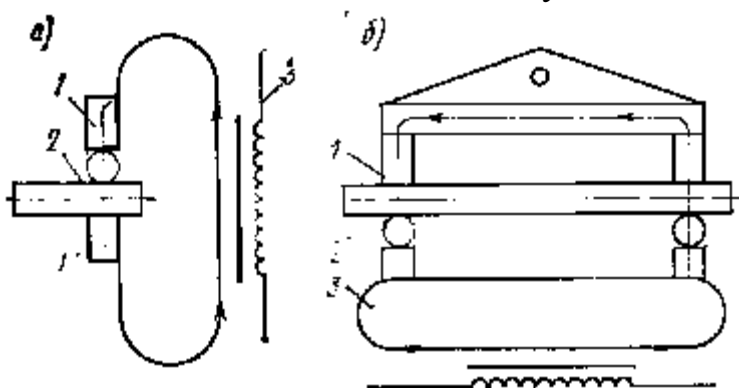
Схема подвода сварочного тока к свариваемым арматурным стержням:
